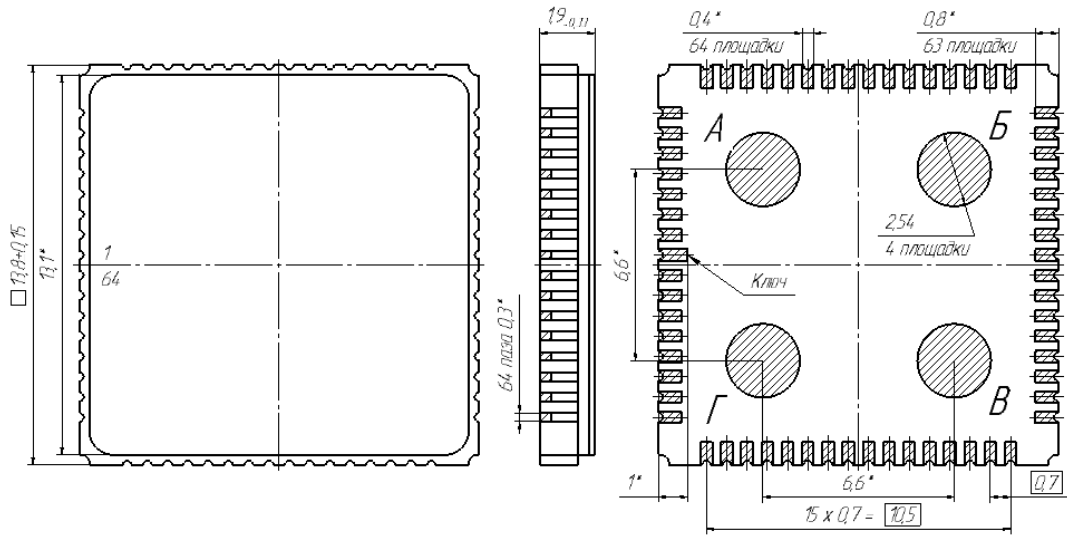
Внешний вид корпуса МК 5153.64-2
